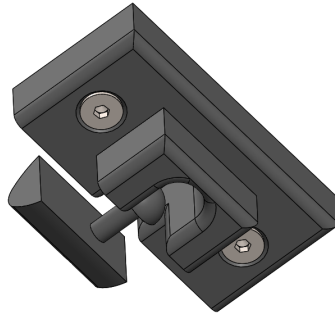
Estructura de aislamiento del sistema. Vista Externa. Elaboración propia.
